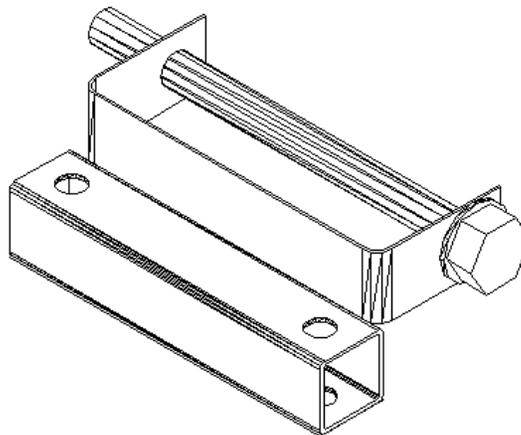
Dibujo de conjunto de pieza que sujeta uno de los lados del alternador
